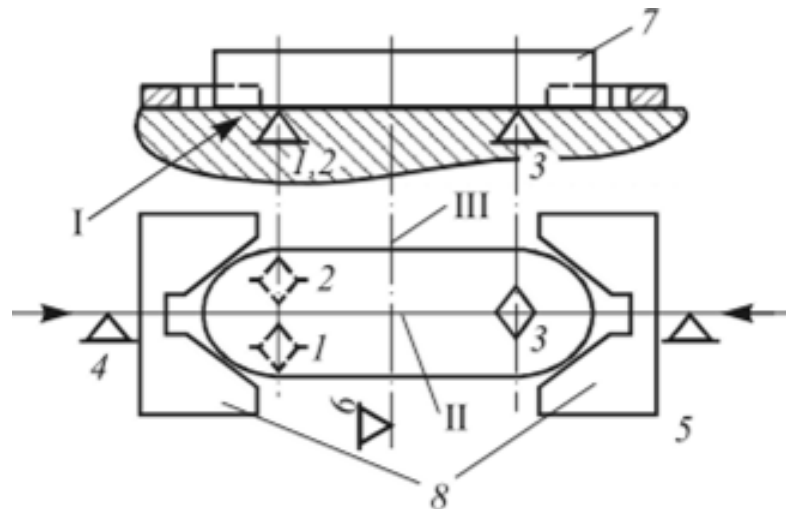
Базування деталі типу «Сережка» у самоцентруючих призмах
